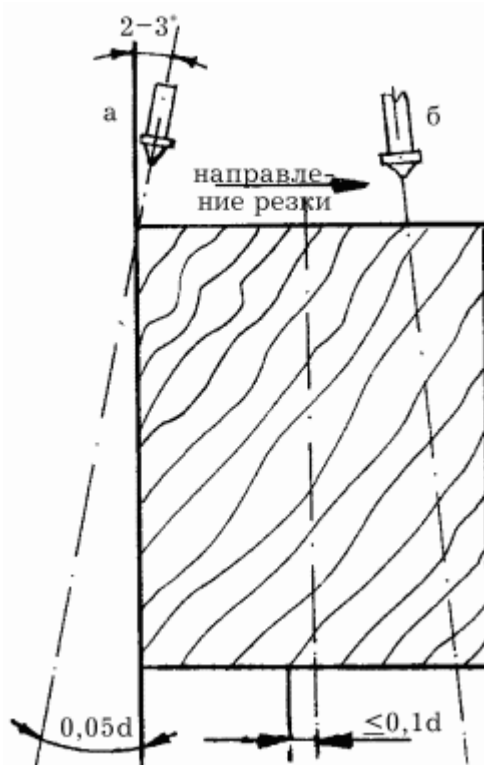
Положение инструмента при резке металла большой толщины: а – перед началом резки; б – перед окончанием резки.
